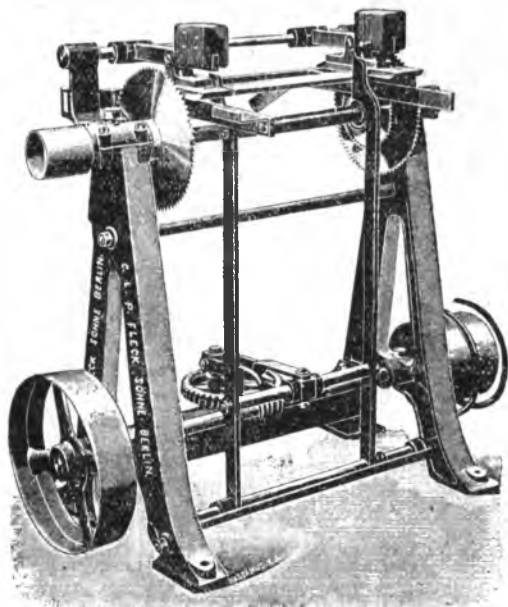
Станок для обрезки клепок, пропиливания утора и скашивания концов.
